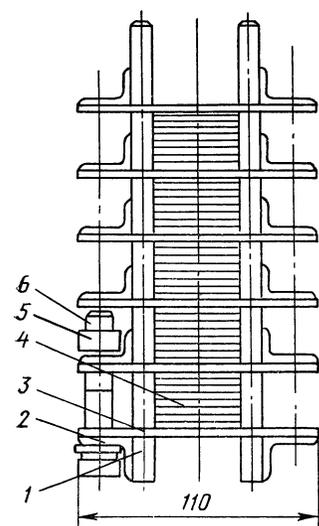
Приспособление для прессовки реек, склеенных клеем из метилцеллюлозы:
